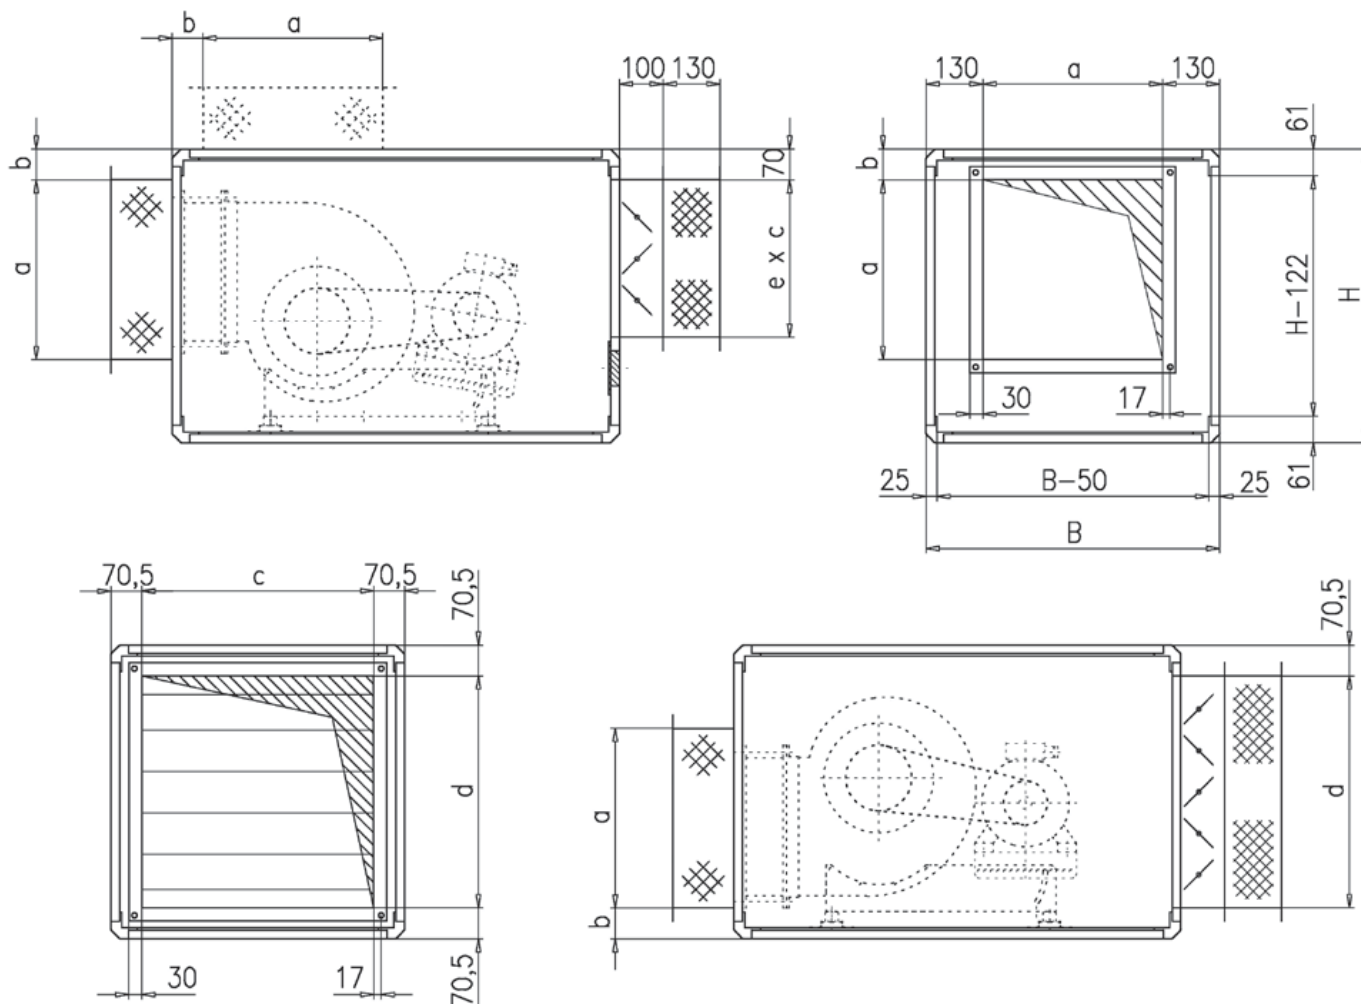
Габаритные и присоединительные размеры установок A20...Q, A20...R
